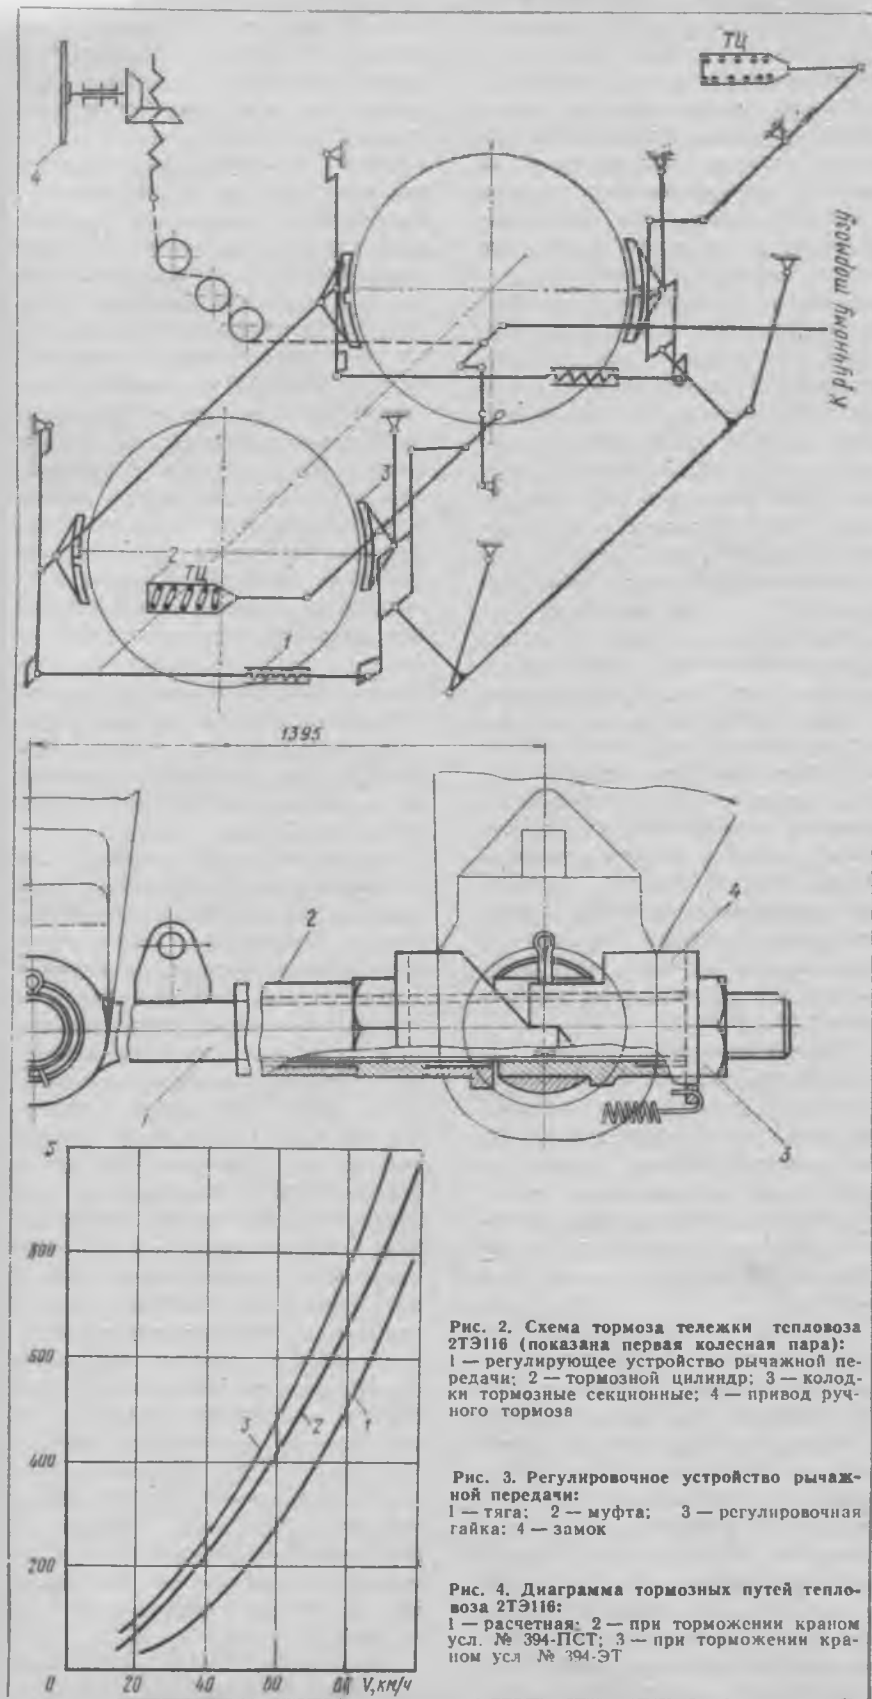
Схема тормоза тележки тепловоза 2ТЭ116 (показана первая колесная пара): 1 — регулирующее устройство рычажной передачи; 2 — тормозной цилиндр; 3 — колодки тормозные секционные; 4 — привод ручного тормоза
